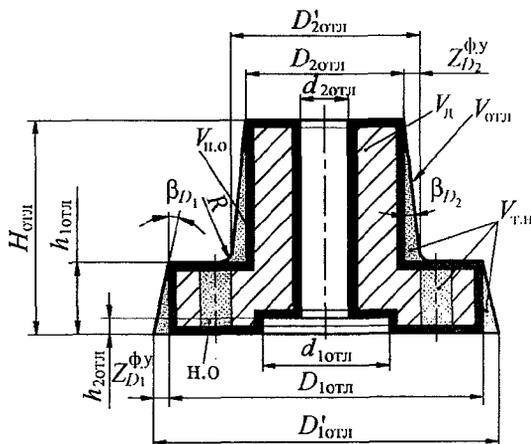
Обозначение размеров и конструктивных элементов отливки, принятые сокращения: отл – отливка; д – деталь; п.о. – припуск на обработку; ф.у – формовочный уклон; т.н – технологические напуски; н.о – непроливаемое отверстие
